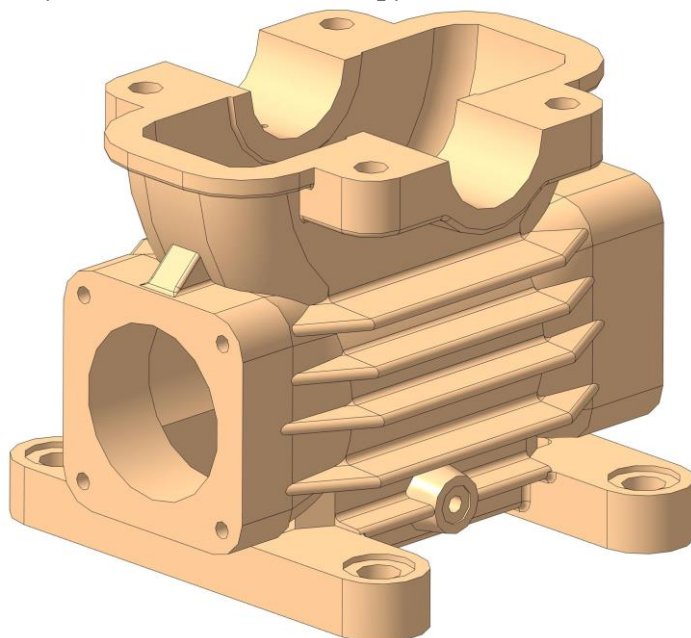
Тривимірна модель корпусу черв'ячного редуктора
